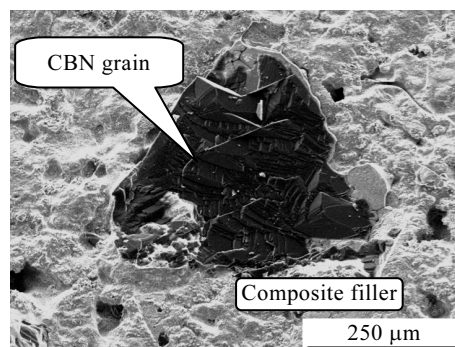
钎焊 CBN 磨粒剪切断口形貌
